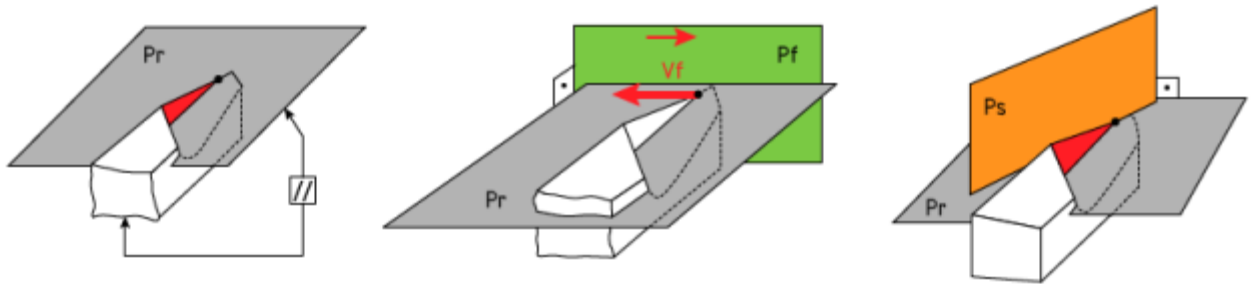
Plan de référence P_r , plan de travail conventionnel P_f , plan de l'arête de l'outil P_s
